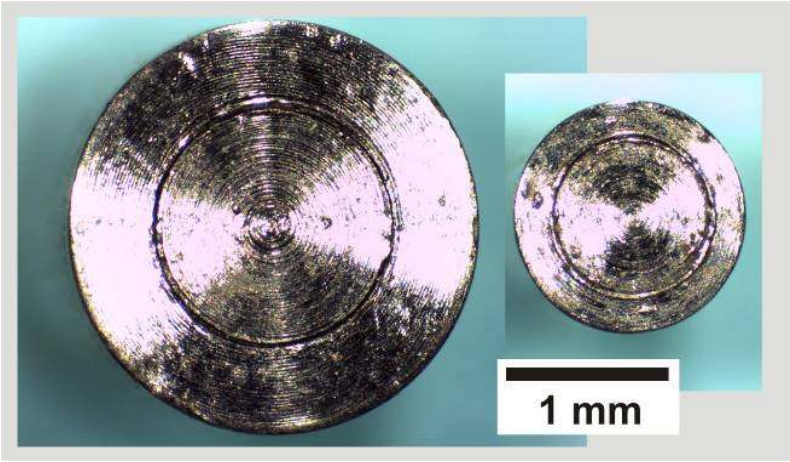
Parte superior de cilindros de 316L antes de ser soldados
